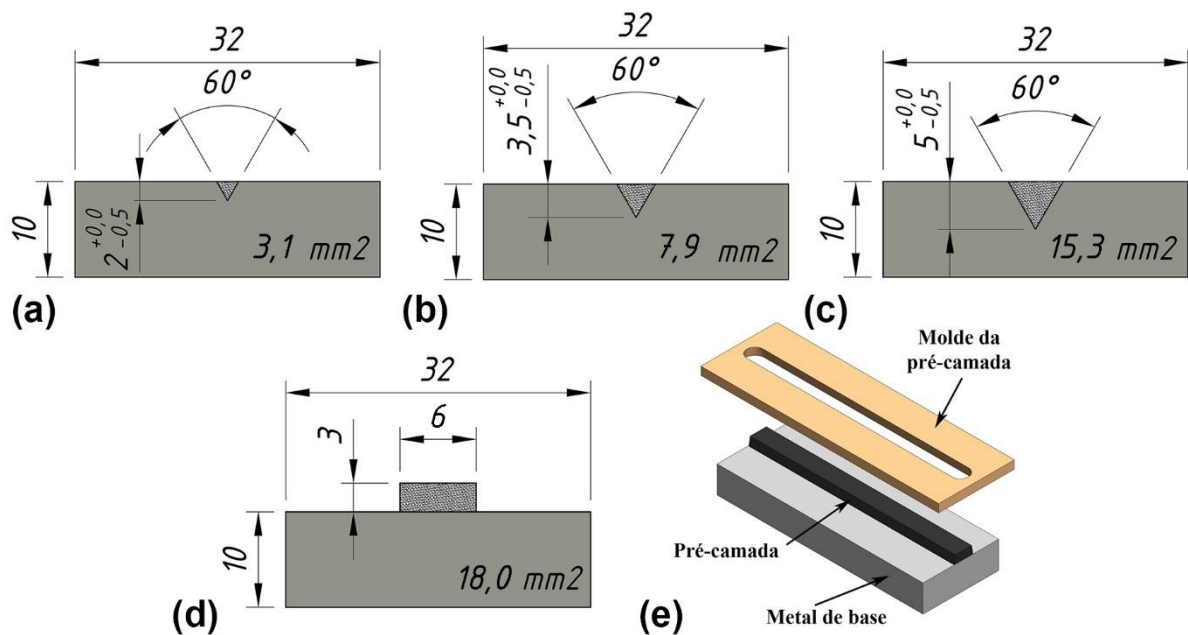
Indicação do metal de base com a deposição do fluxo para a soldagem GTAW (dimensões em milímetros). (a) GCC-TiCV1. (b) GCC-TiCV3. (c) GCC-TiCV5. (d) GCC-TiCSC.
